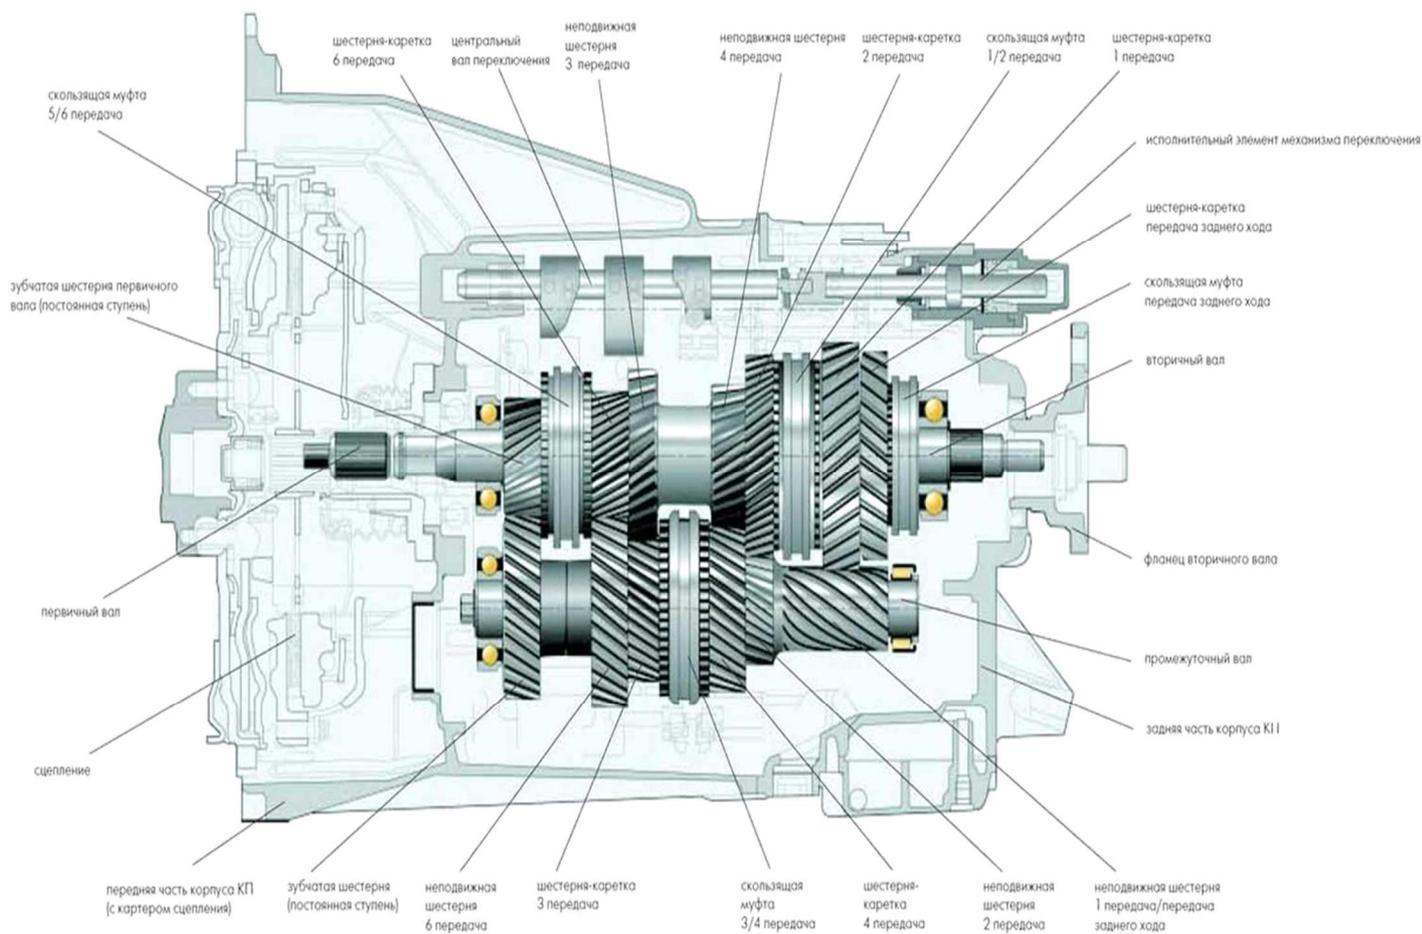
Конструктивная схема шестиступенчатой коробки передач
